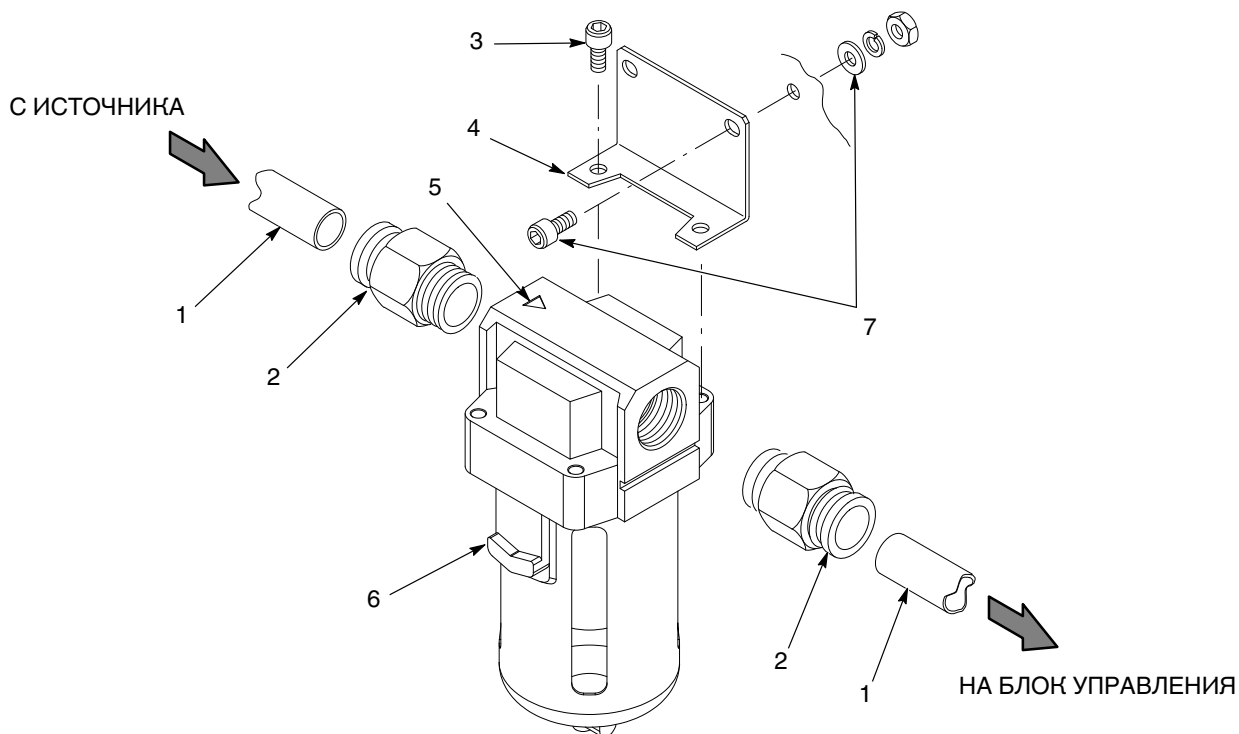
Монтаж воздушного фильтра – системы для монтажа на стене и на поручне
